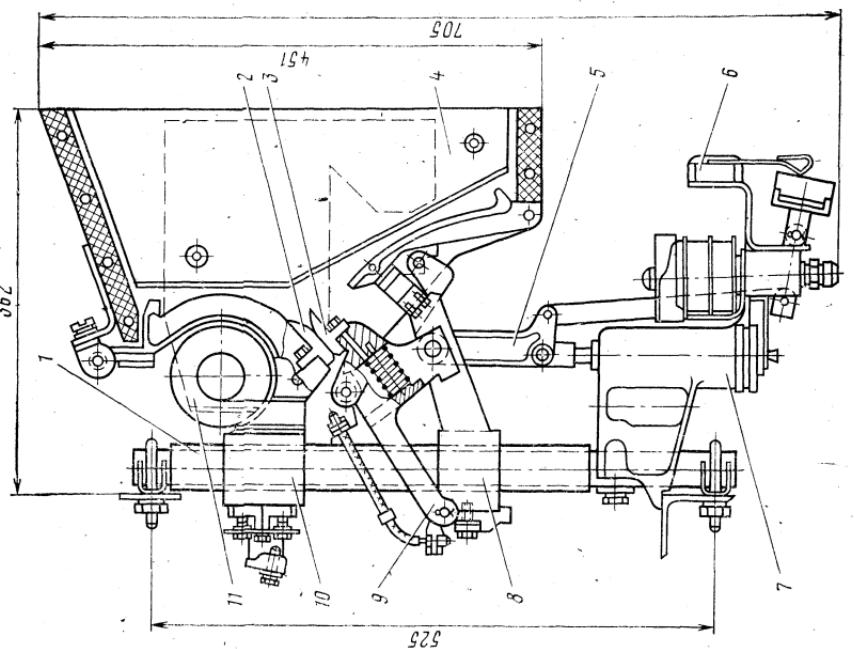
Электропневматический контактор ПК-06 (ПК-07—ПК-11, ПК31—ПК-36):
